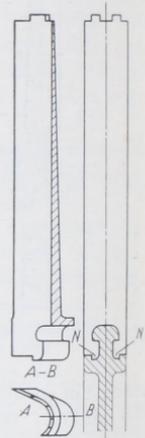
Schaufelbefestigung der Bergmann-Werke Berlin.
